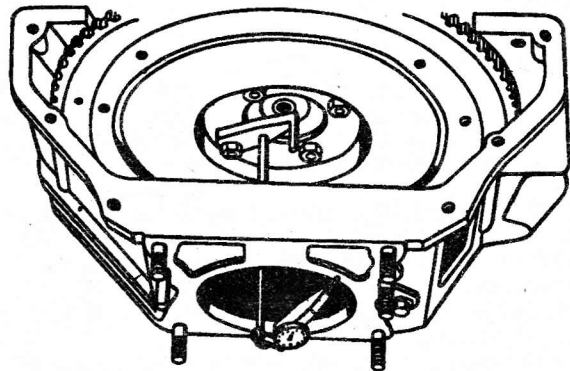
Проверка перпендикулярности заднего торца картера сцепления к оси коленчатого вала
